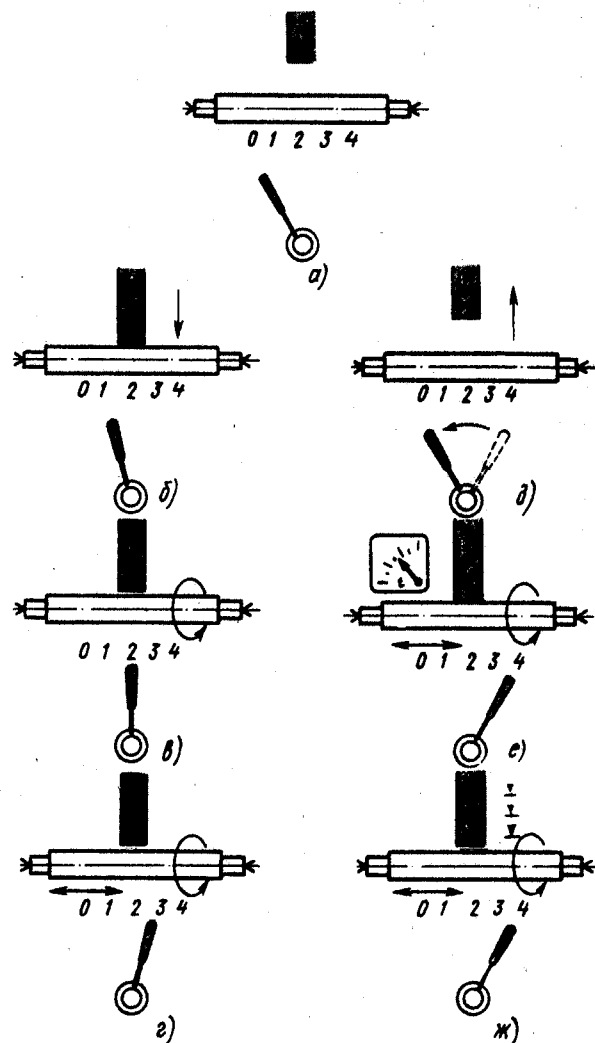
Разные положения рукоятки управления движением подачи круглошлифовального станка
